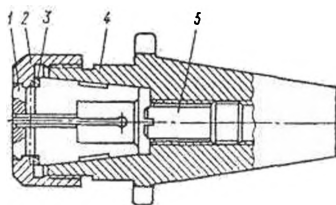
Цанговий патрон для кріплення інструментів з циліндричним хвостовиком
